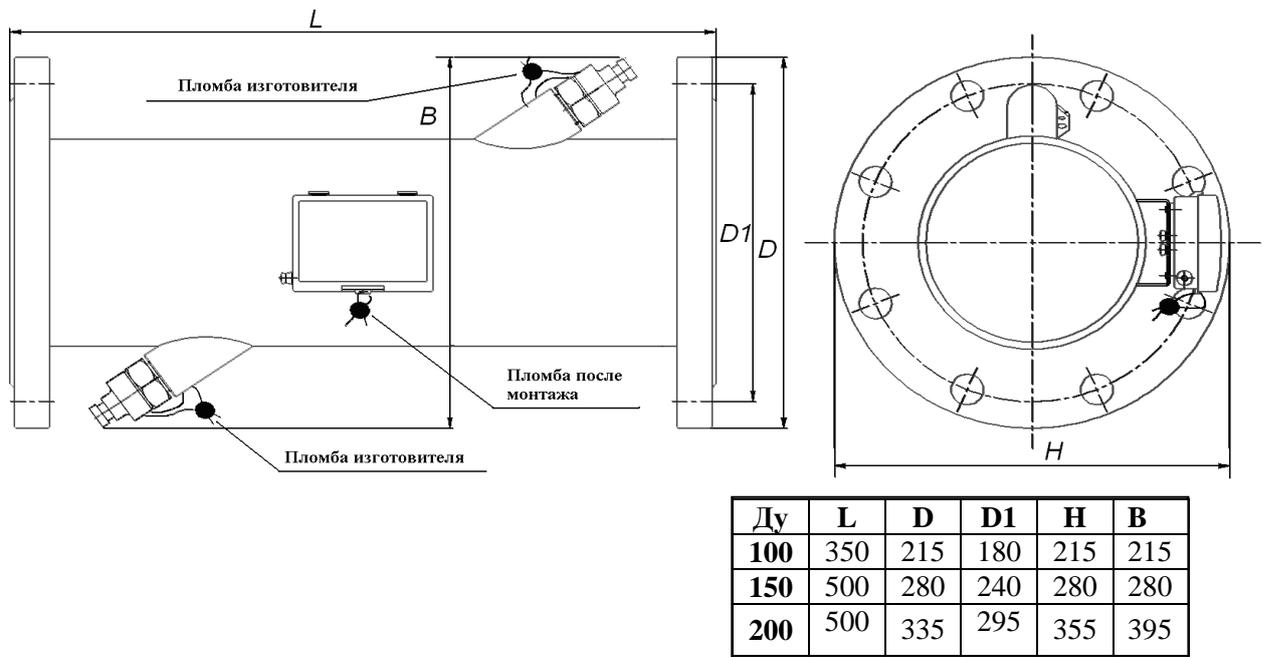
Габаритные размеры ультразвукового преобразователя расхода с Ду100, Ду150, Ду200 (Стальной корпус)
